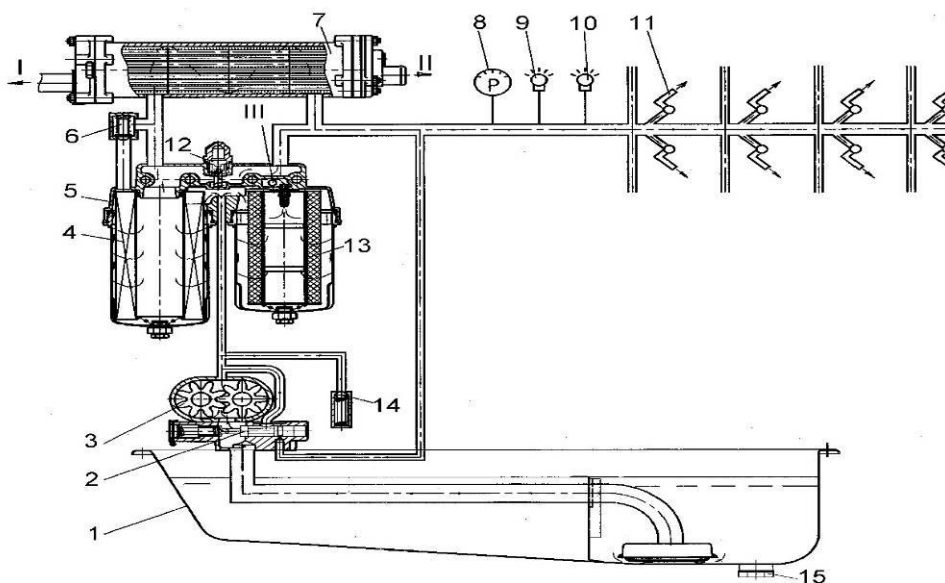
Смазочная система двигателя автомобиля КАМАЗ-Евро-1
